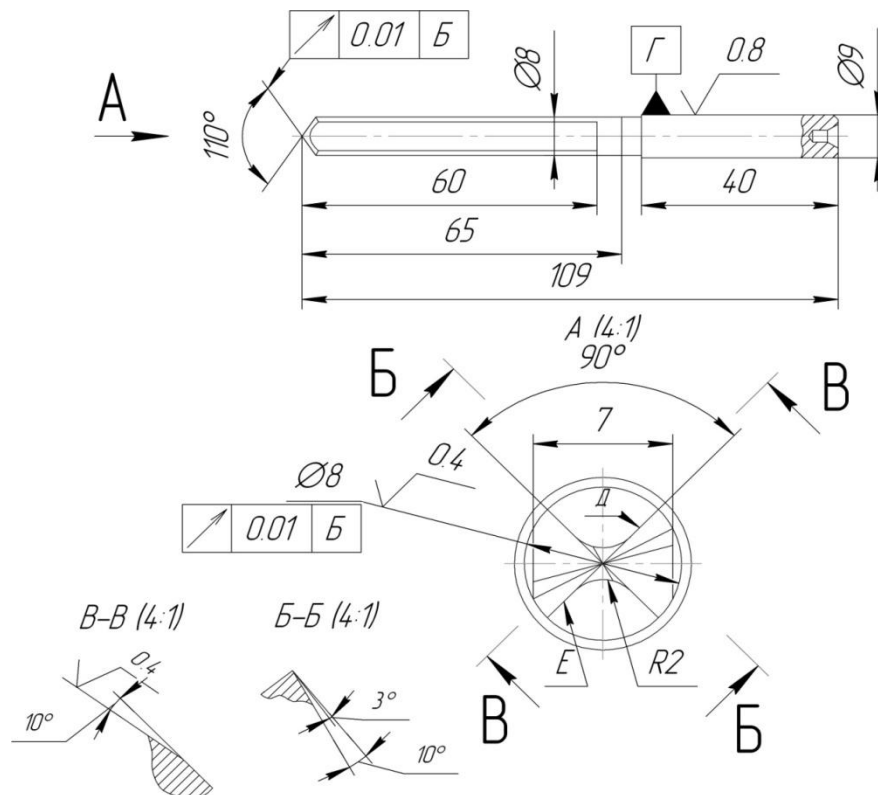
Креслення реверсивного свердла розробленої конструкції
